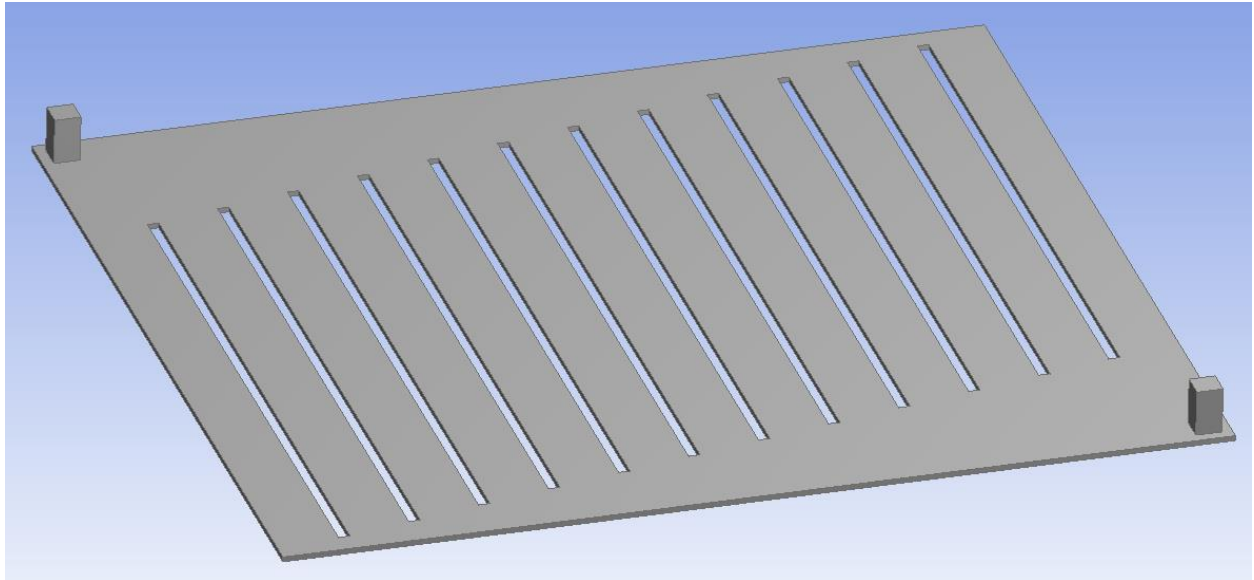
Cubierta Plana 2 con Canales 0,6 m
